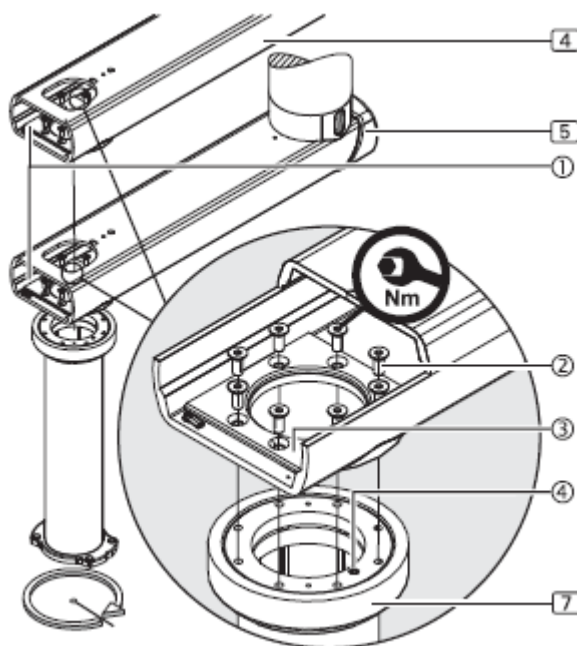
Assemblage du tube de descente sur les bras NON motorisés
